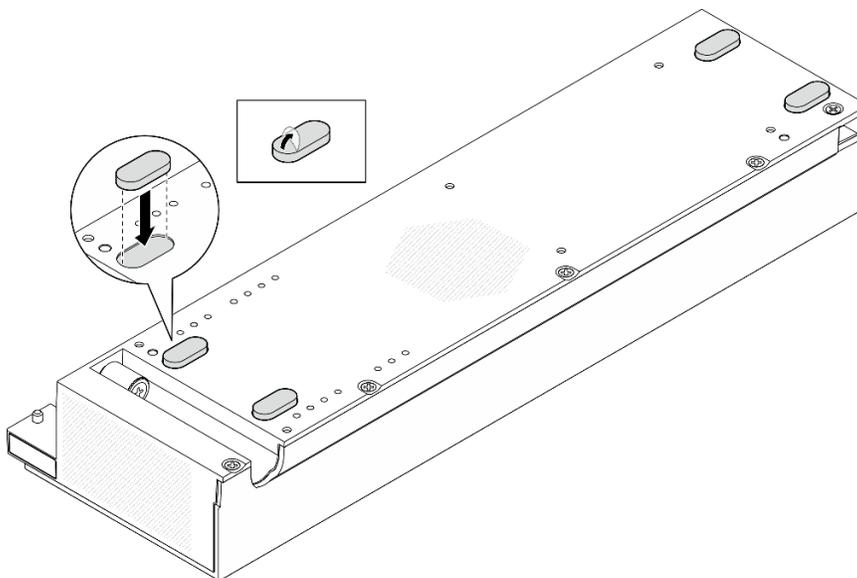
Installation des pieds en caoutchouc sur le kit d'extension PCIe
